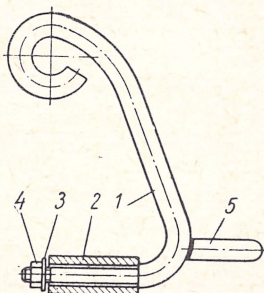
Приспособление для установки и снятия патрона токарного станка
